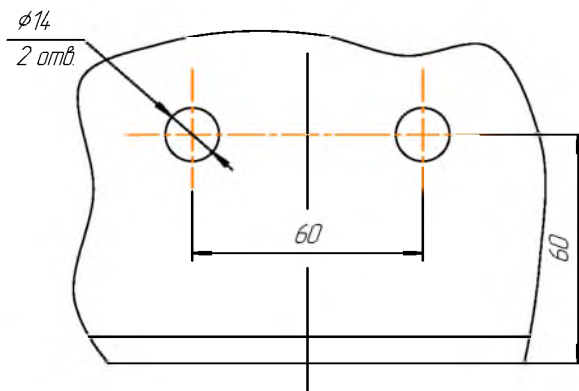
Отверстия для заземления полюсов к опорной конструкции
